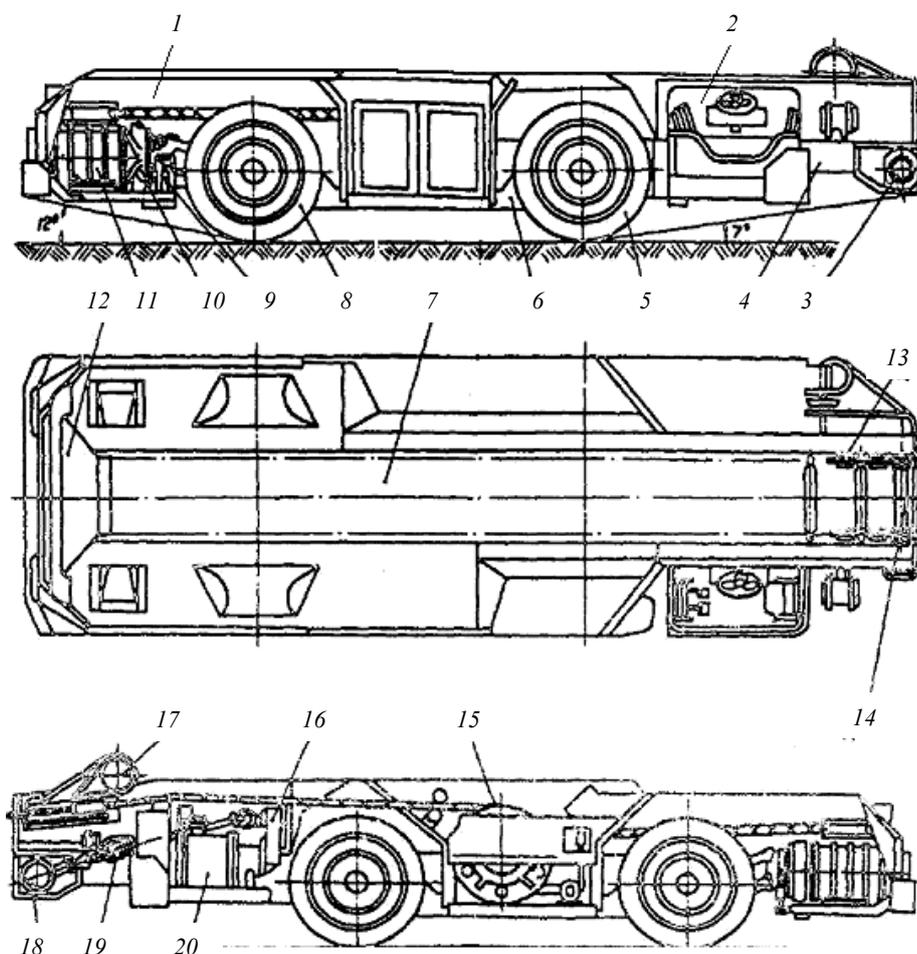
Общий вид шахтного самоходного вагона 5ВС-15М: 1 – борт боковой кузова; 2 – кабина; 3 – редуктор планетарный скребкового конвейера; 4 – рама кузова; 5 – мост передний ходовой части; 6 – подрамник передний рамы ходовой части; 7 – часть кузова расширенная; 8 – мост задний ходовой части; 9 – тормоз стояночный; 10 – редуктор привода хода; 11 – электродвигатель привода хода; 12 – борт кузова задний; 13 – орган тяговый донного скребкового конвейера; 14 – вал приводной донного скребкового конвейера; 15 – барабан кабельный системы намотки кабеля; 16 – редуктор промежуточный привода конвейера; 17 – выводное устройство питающего кабеля; 18 – редуктор конический привода конвейера; 19 – редуктор планетарный привода конвейера; 20 – электродвигатель привода конвейера
